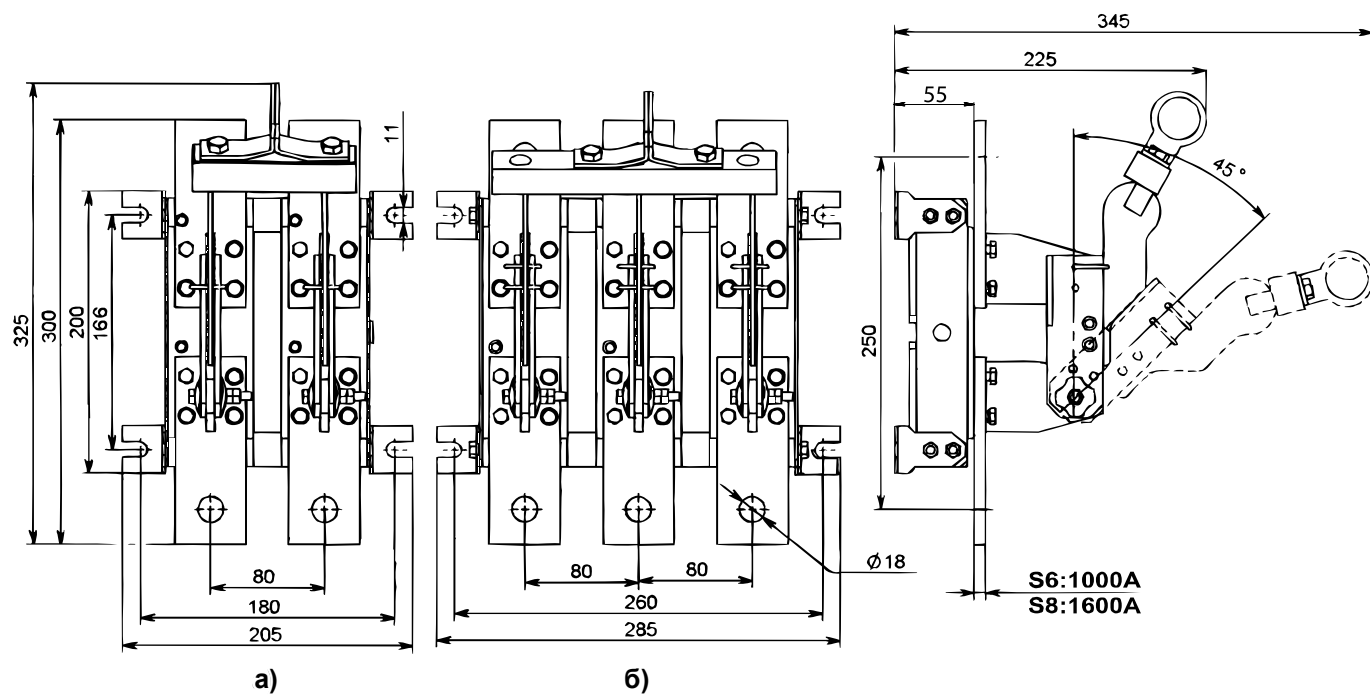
Разъединитель PE19 с центральным рычагом для управления штангой
